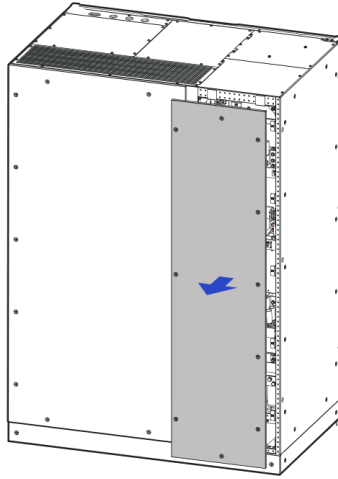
Retiro de la cubierta del cableado del UPS-IND HF 13500 y 13600
